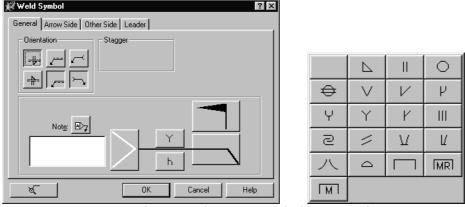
Indicações da Junta Soldada e tipos de Junta
